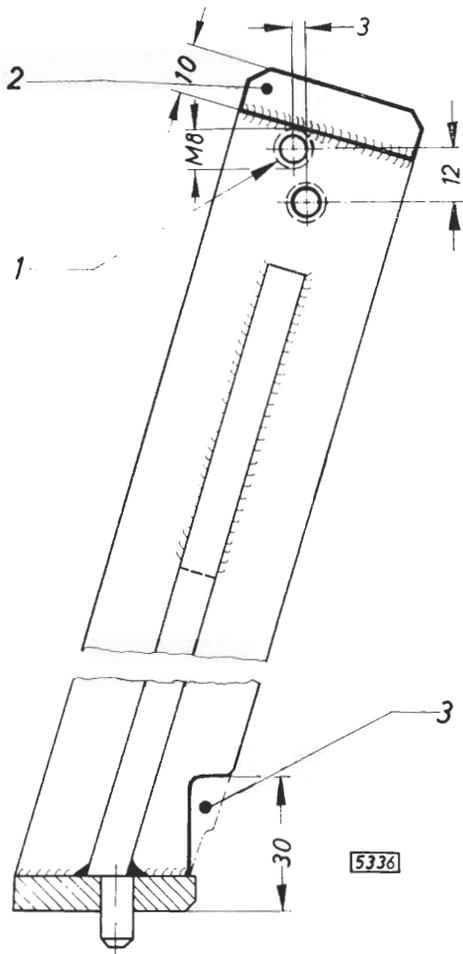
Vorderrahmen-Schweißlehre S-1285
